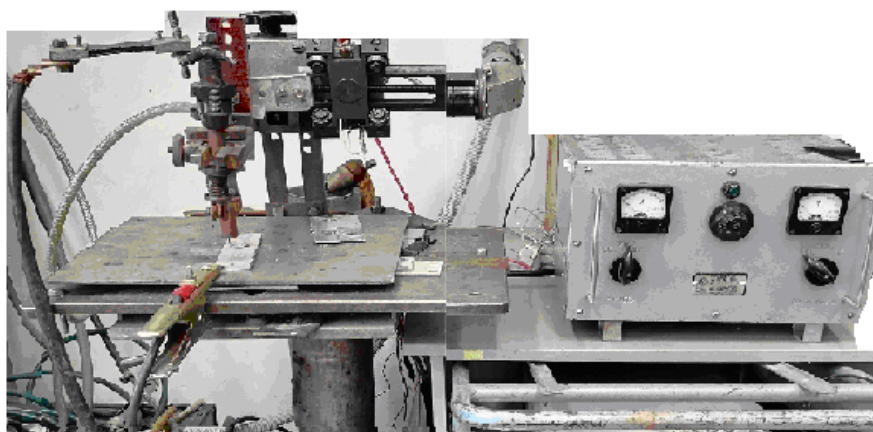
Лабораторный стенд с блоком питания привода ВСА
